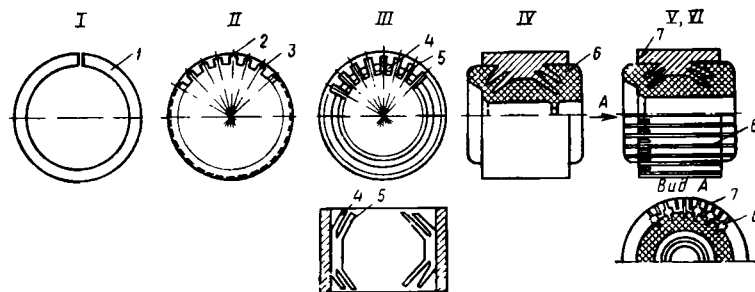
Последовательность операций при изготовлении коллектора из неразделенной заготовки гибкой полосы:
